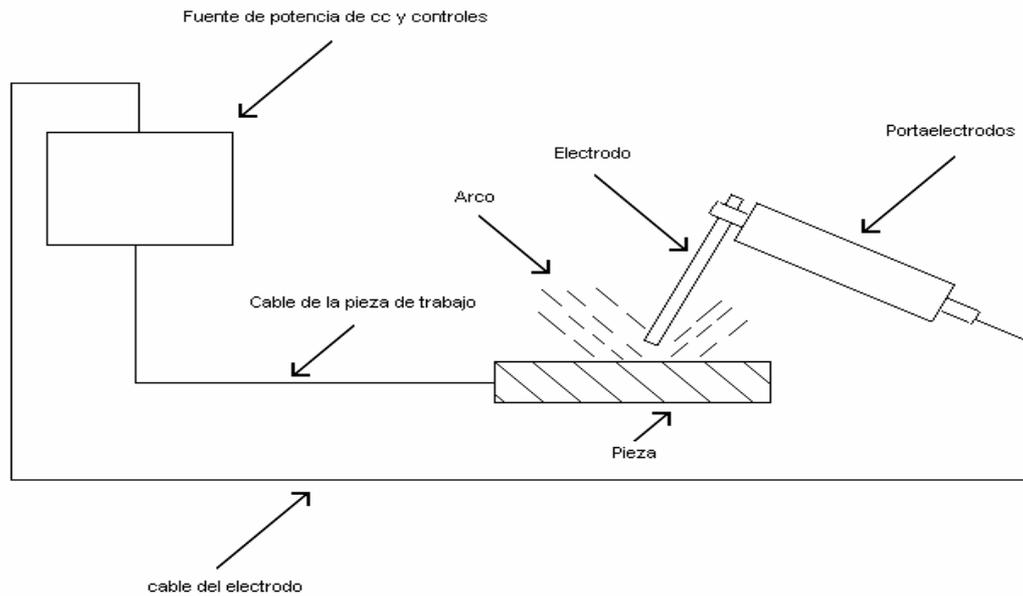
Elementos de un circuito de soldadura típico para soldadura de metal protegido
